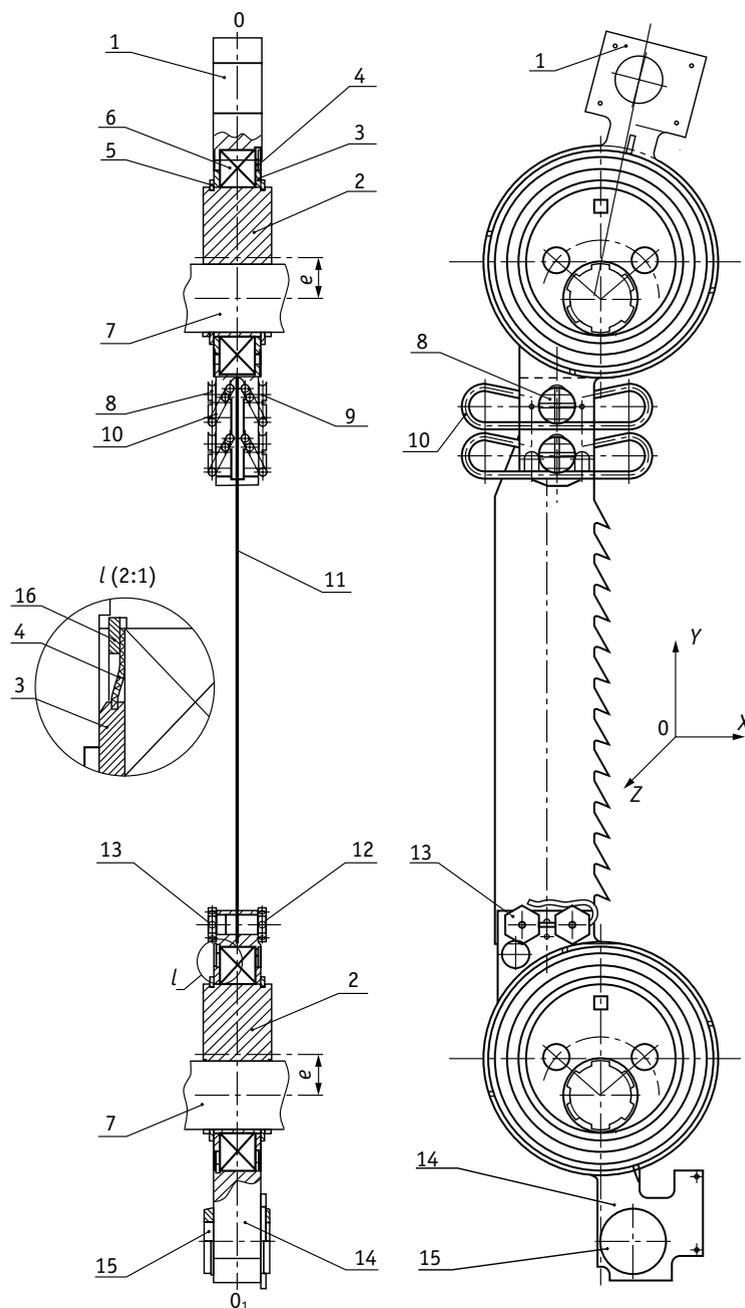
Главный узел пильного блока: 1 – верхний шарнирный узел, 2 – эксцентрик, 3 – кольцо, 4 – кольцо пыльник, 5 – пружинное кольцо (запорное), 6 – радиально-упорный подшипник, 7 – вал шлицевой, 8, 9 – крепеж верхнего шарнирного узла, 10 – упругий элемент (скоба), 11 – пильное полотно, 12, 13 – крепеж нижнего шарнирного узла, 14 – нижний шарнирный узел, 15 – устройство баланса (корректирующая масса) со шпилькой, 16 – пружинное кольцо (запорное)
